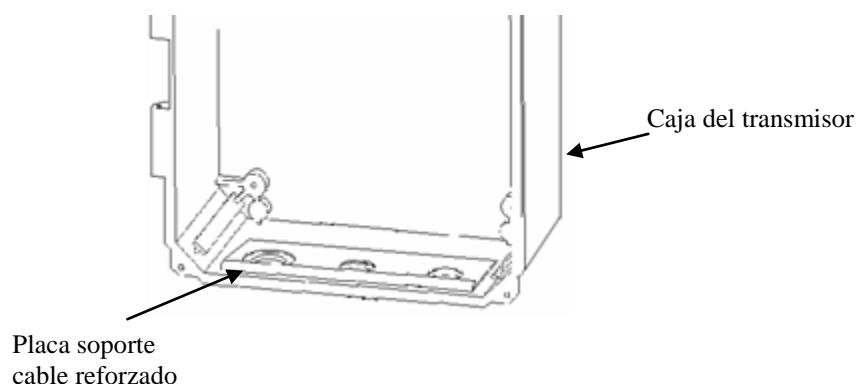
Instalación de la Placa Enderezadora del Cable Blindado
